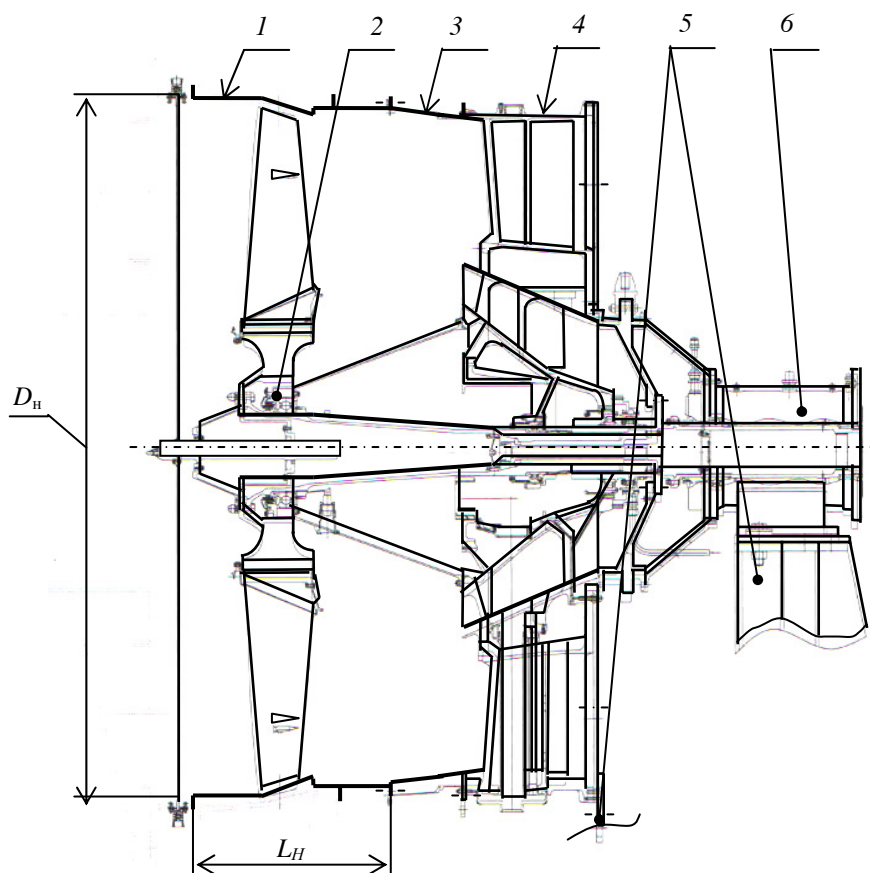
Схема установки для испытаний корпуса вентилятора: 1 – корпус вентилятора; 2 – рабочее колесо вентилятора; 3 – корпус спрямляющего аппарата; 4 – разделительный корпус; 5 – элементы рамы установки; 6 – электропривод
